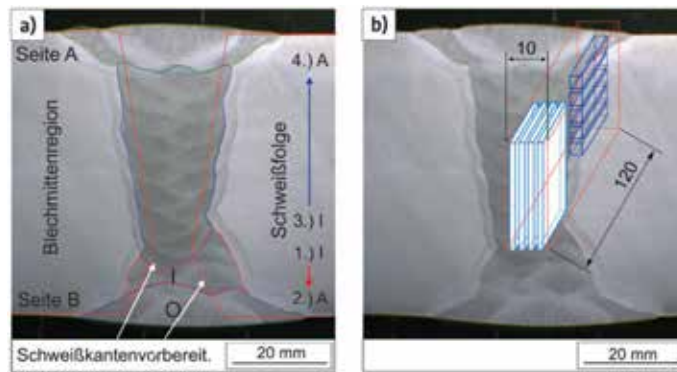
• Probengeometrie; a) Schliffbild Schweißnaht, b) Probenlage.
